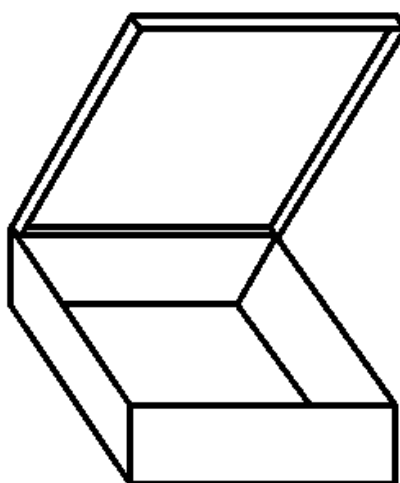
Эскиз корпуса с крышкой с отбортовками
